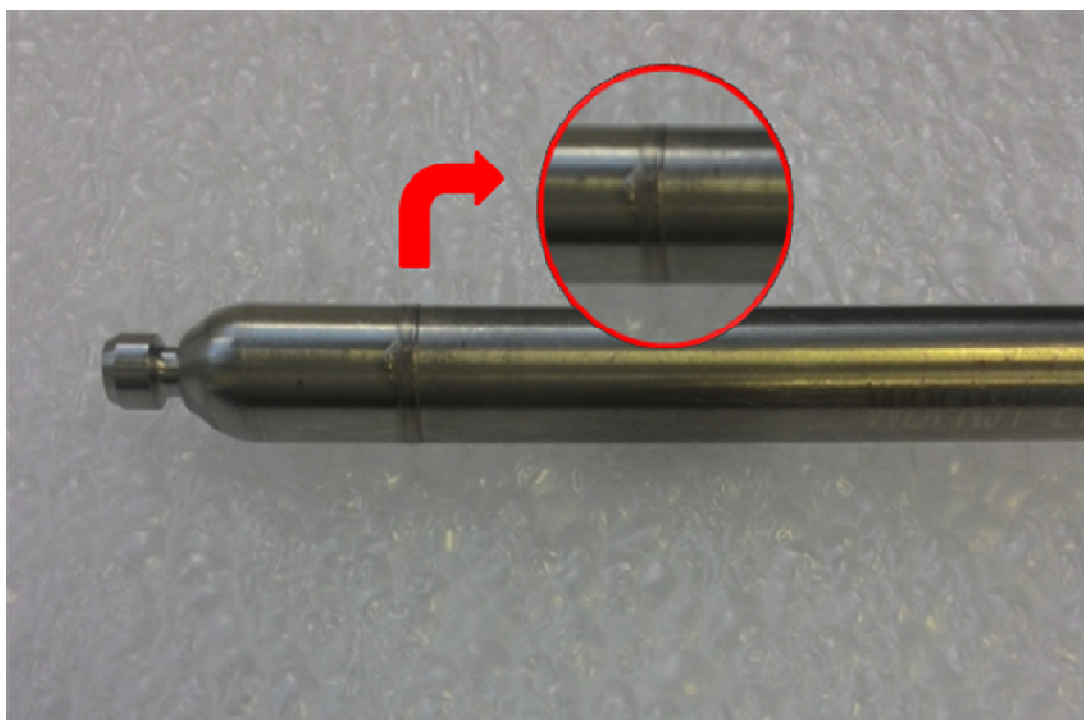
CP soldado por resistência e pressão com a presença de fusão sobre o Tampão Terminal
